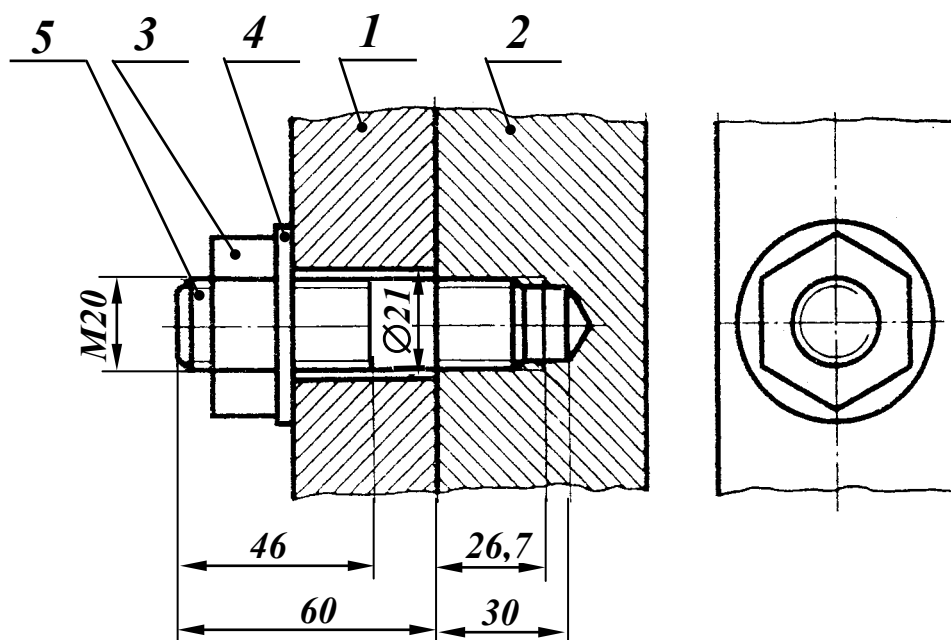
Нанесение размеров на чертеже «Соединение шпилькой»
